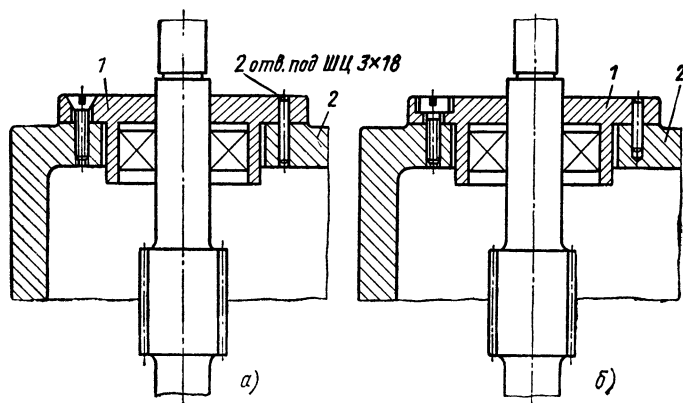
Конструкции крепления кронштейна 1 к корпусу 2
